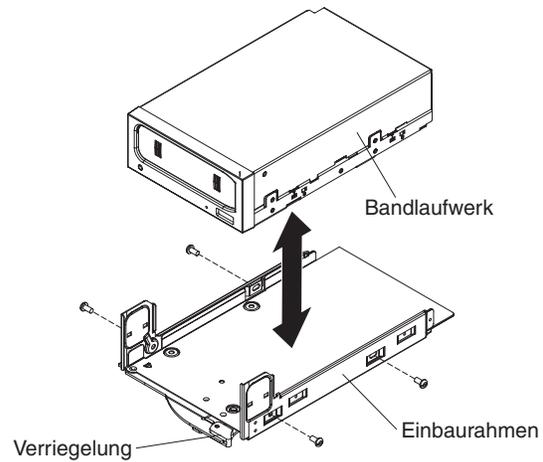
Bandlaufwerk im Einbaurahmen installieren
